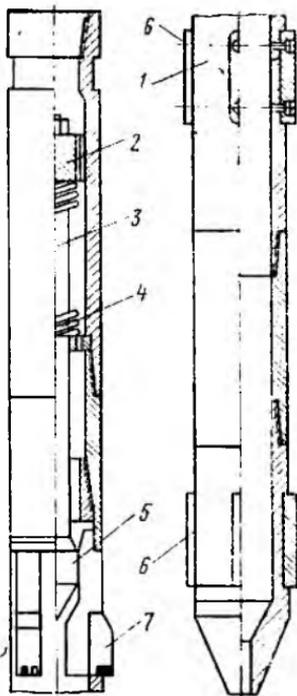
Универсальное вырезающее устройство: 1 — разъемный корпус; 2 — поршень; 3 — шток; 4 — возвратная пружина; 5 — толкатель; 6 — центраторы; 7 — резцы
